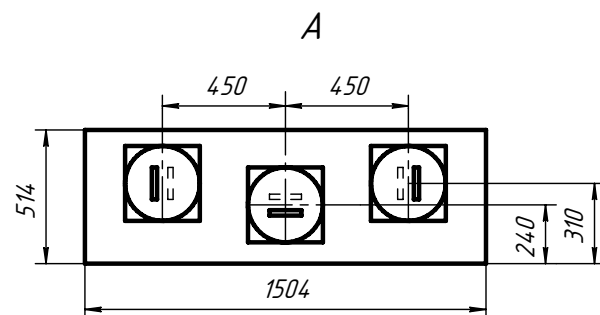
Габаритные, установочные, присоединительные размеры шкафов.
